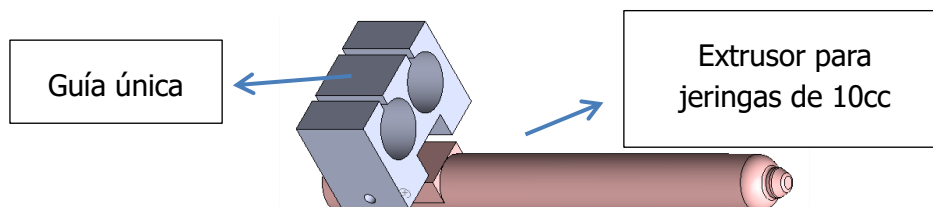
Ensamblaje guía y extrusor para la jeringa de 10cc.
